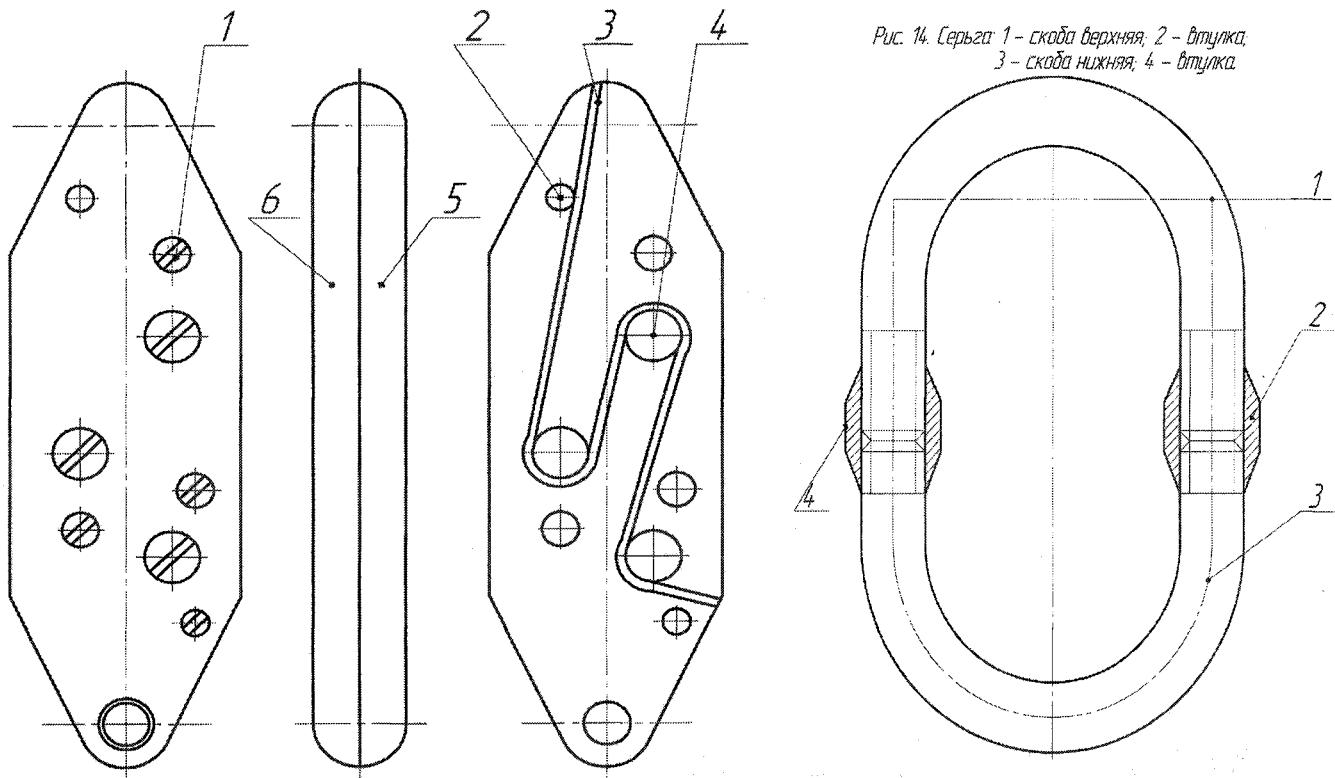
Карабин: 1 – винт; 2 – ограничительная шпилька; 3 – канавка для каната; 4 – полец; 5 – крышка; 6 – корпус.
